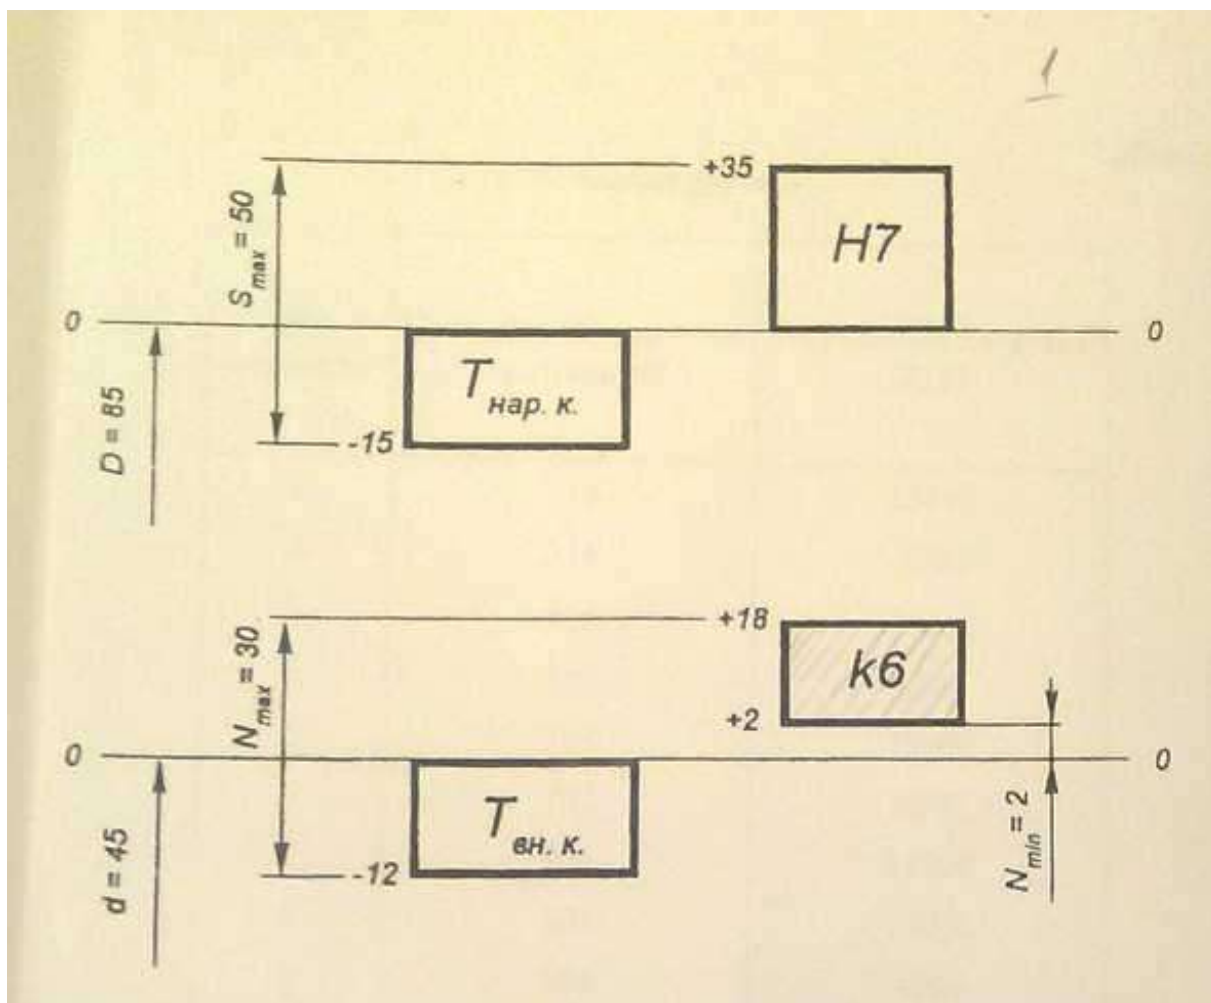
Схема расположения полей допусков и посадочных размеров подшипников и сопряженных деталей.
